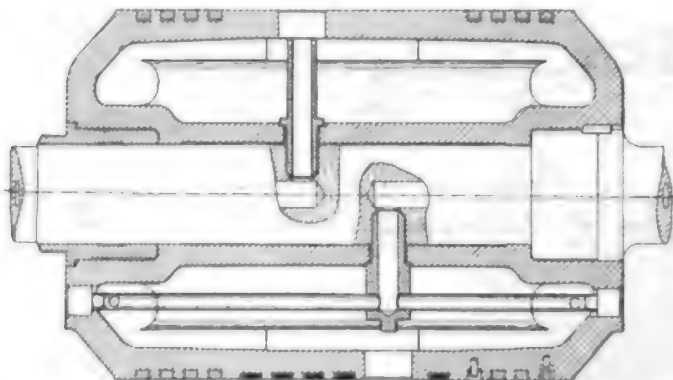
Kolben einer Körtingmaschine mit Weißmetallfütterung, ausgeführt von der Gutehoffnungshütte in Oberhausen.
